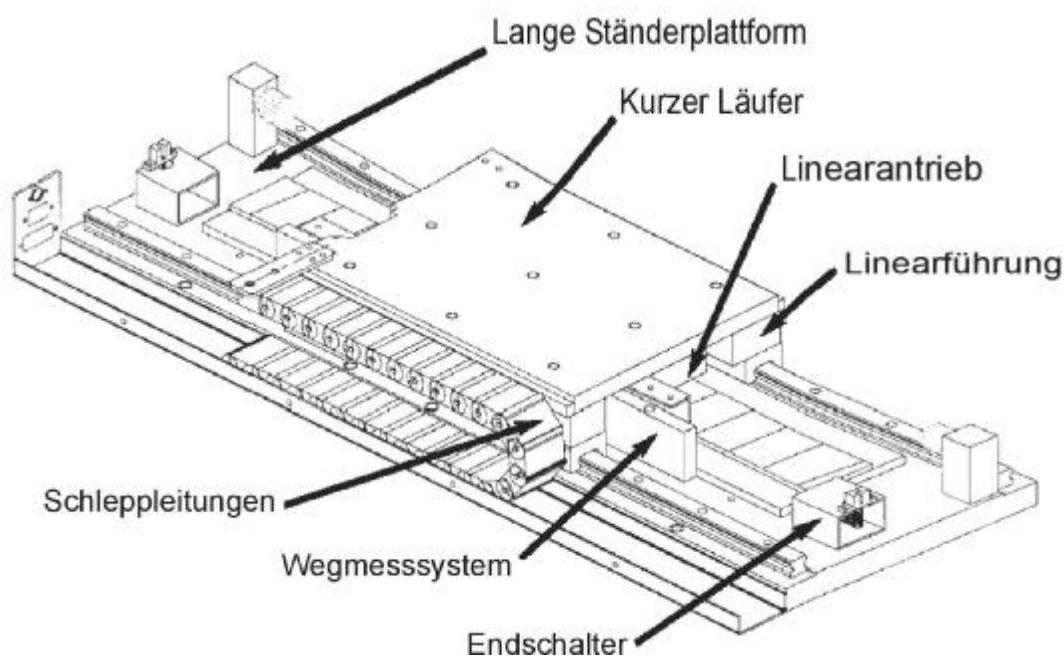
Prinzip handelsüblicher linearer Synchronmotoren mit langem Permanentmagnet-Ständer [BAL03]
